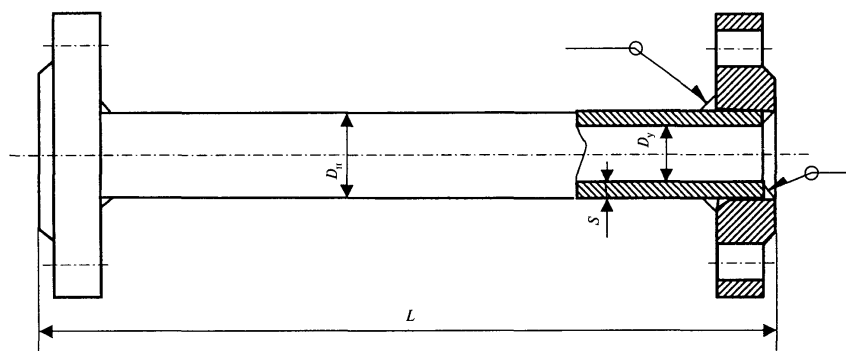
Схема трубы с приваренными фланцами (тип А)
